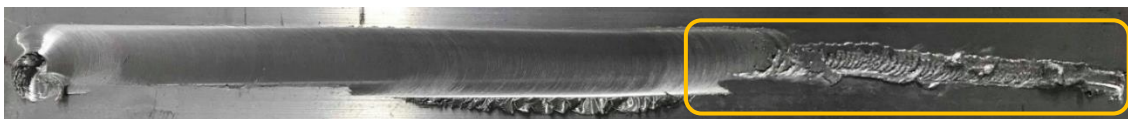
Zone à rejeter d'une soudure faite avec le robot avec 750 rpm et 270 mm/min
